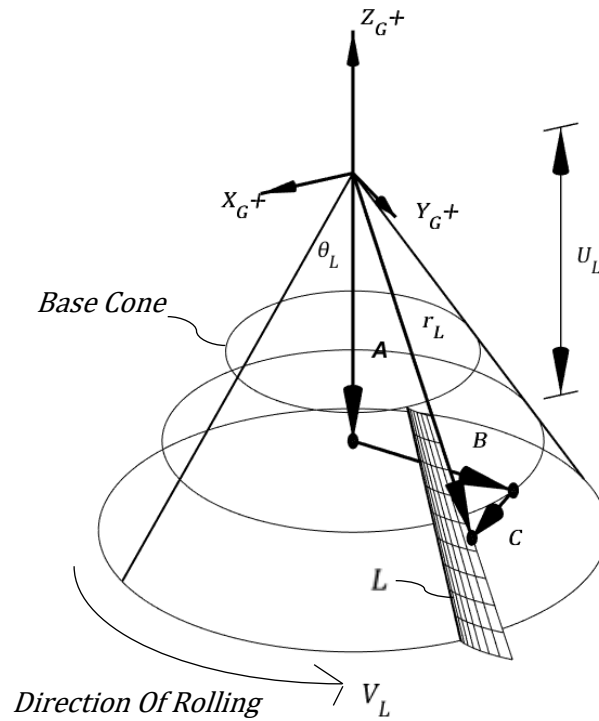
Superficie paramétrica del flanco del diente del engranaje
